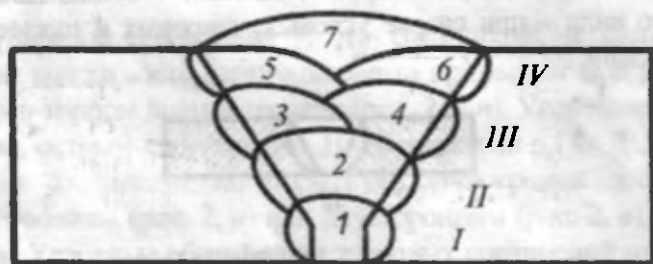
Многослойный сварной шов: 1-7 – последовательность выполнения переходов; I – IV – слои; 1 – корневой шов; 7 – облицовочный шов
